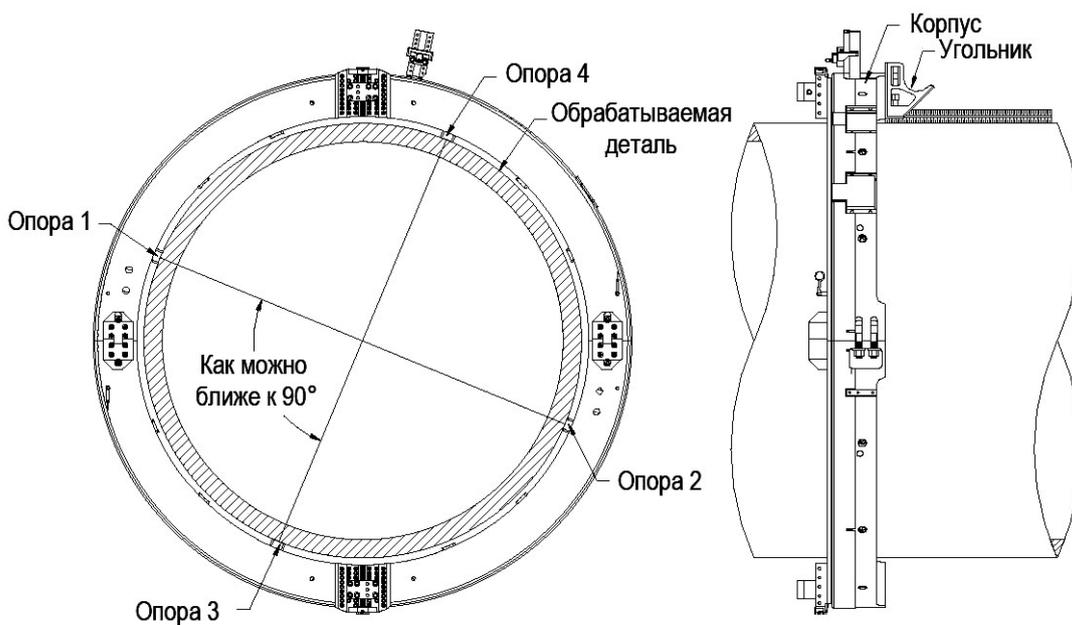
Схема центровки и проверки перпендикулярности корпуса станка поверхности трубы
